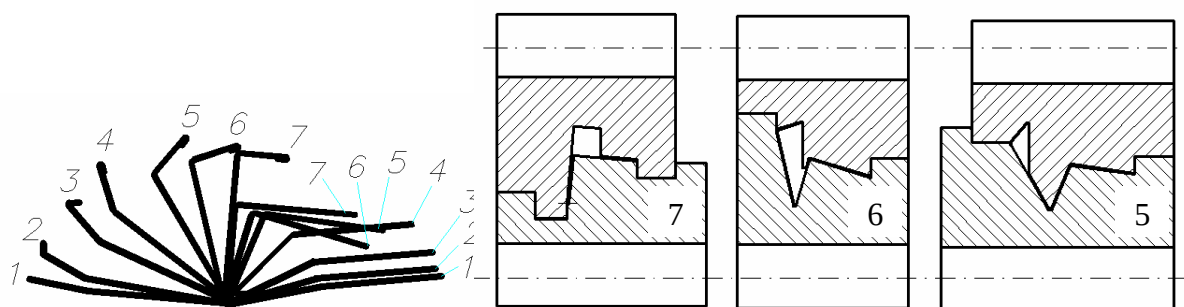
Розеточная схема формообразования и валковые калибры с зонами высвобождения для изготовления F-образного профиля
